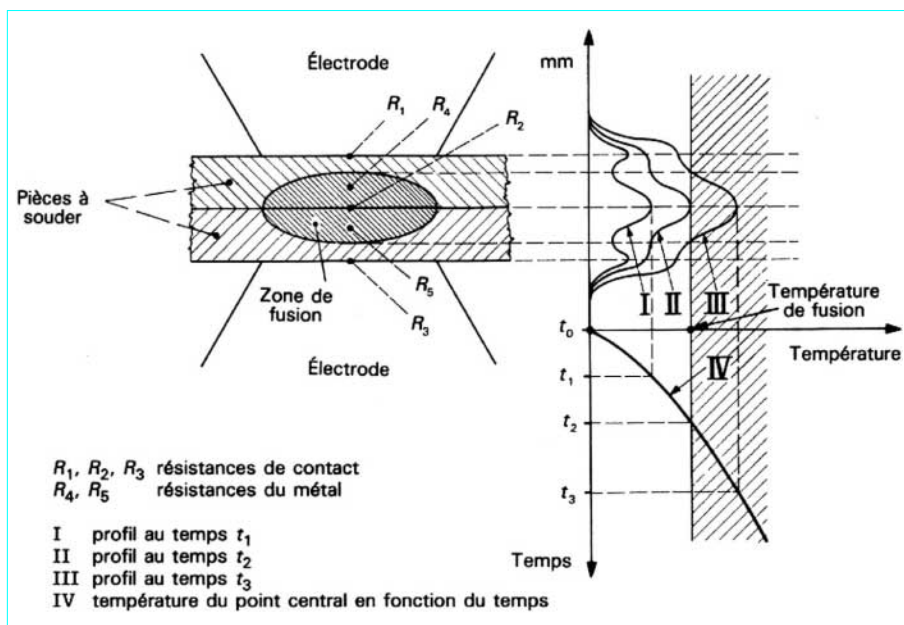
Soudage par points : formation d'un point de soudure
